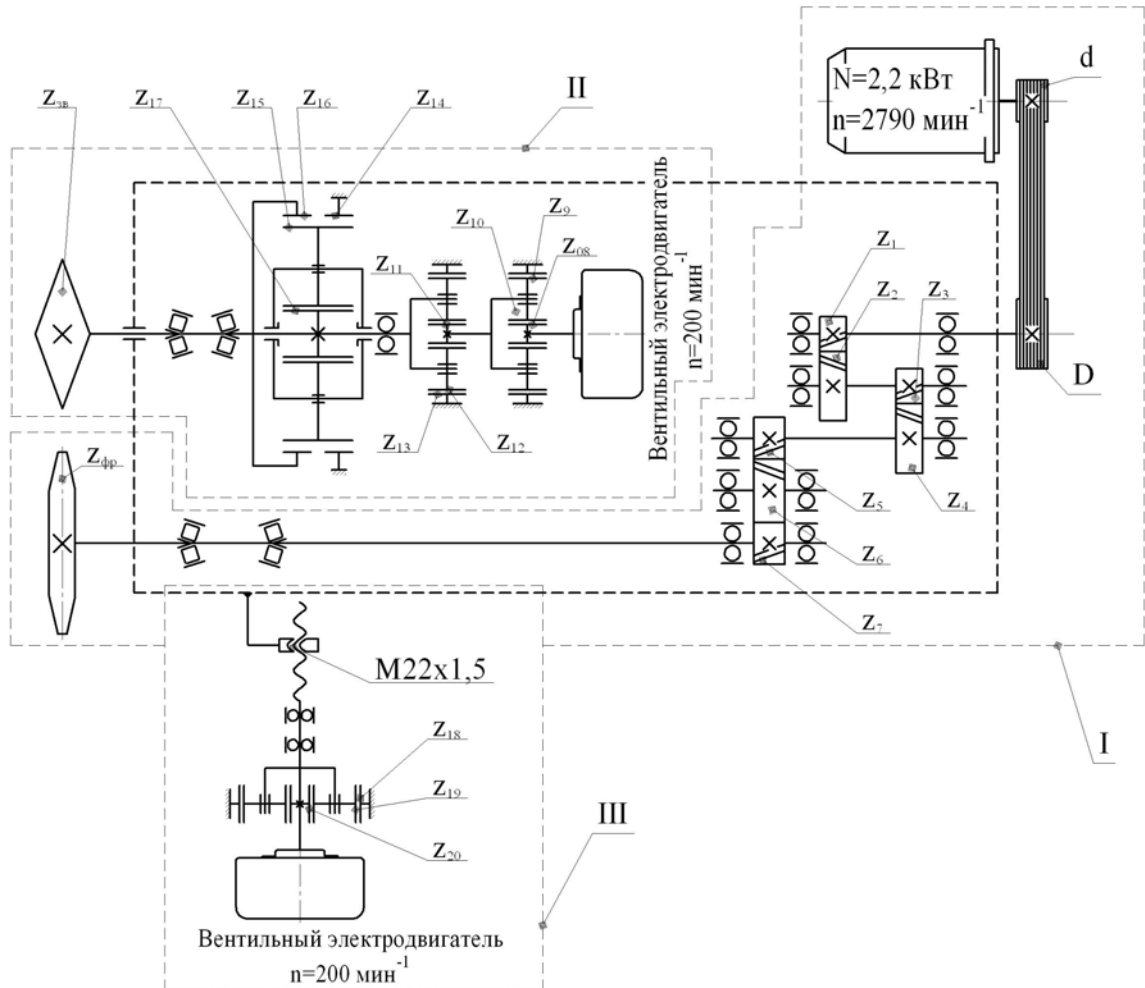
Кинематическая схема машины новой конструкции
